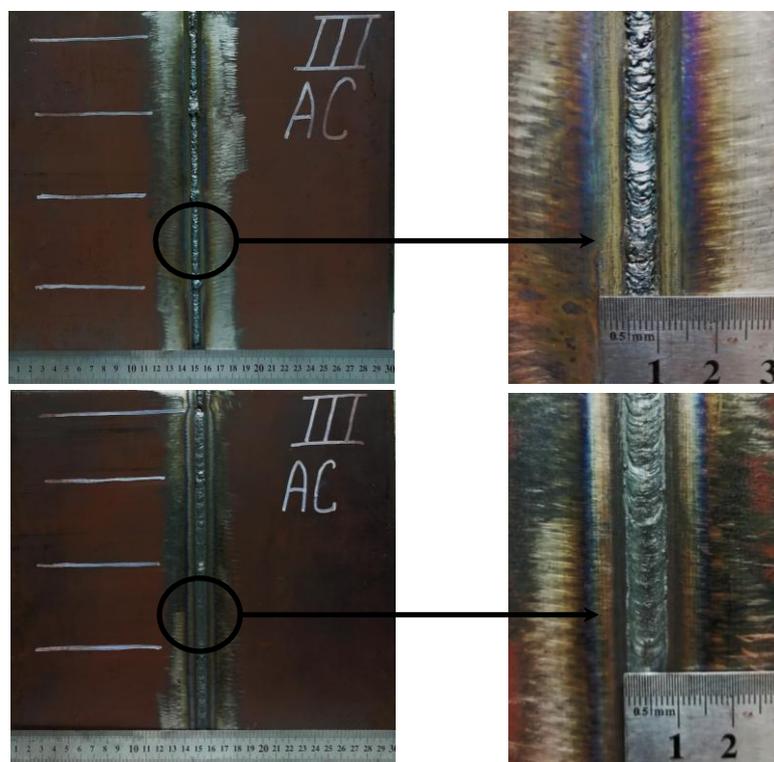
Лицевая сторона и обратный валик сварного соединения, выполненного на переменном прямоугольном токе
